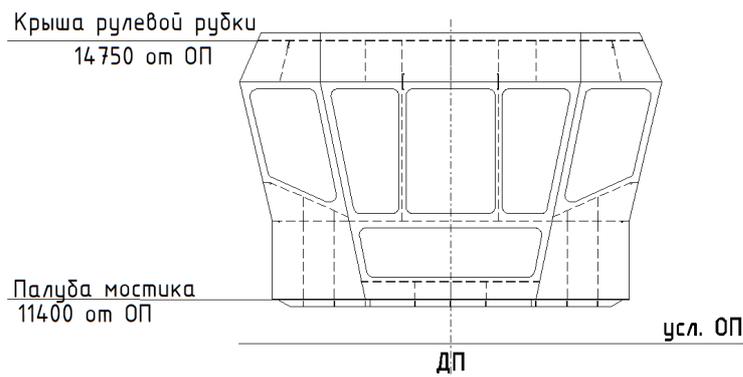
Конструктивный чертеж кормовой стенки рулевой рубки.
